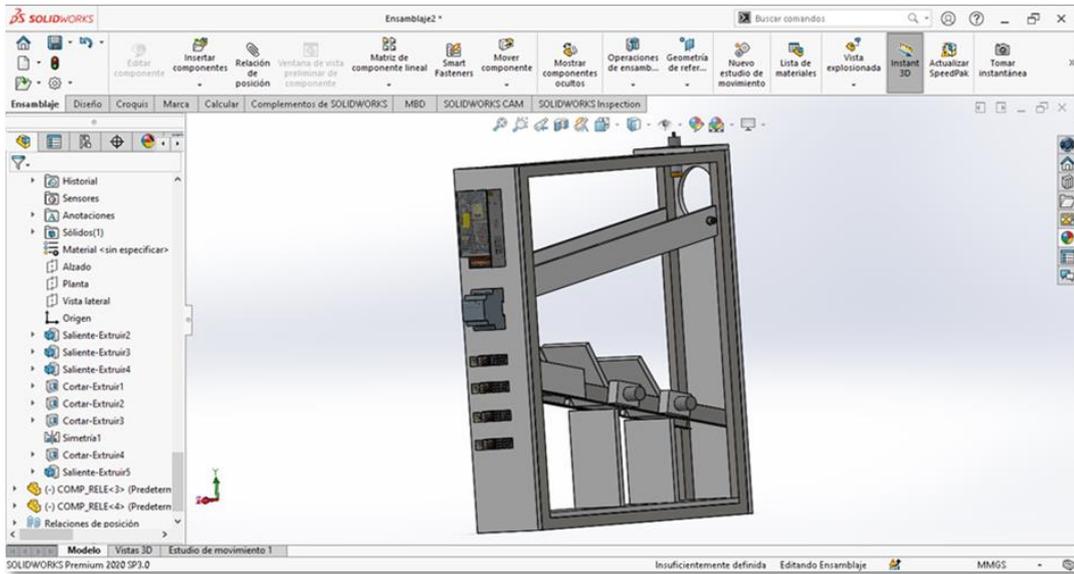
Proyecto ensamblaje – Solidworks (Vista 2)
